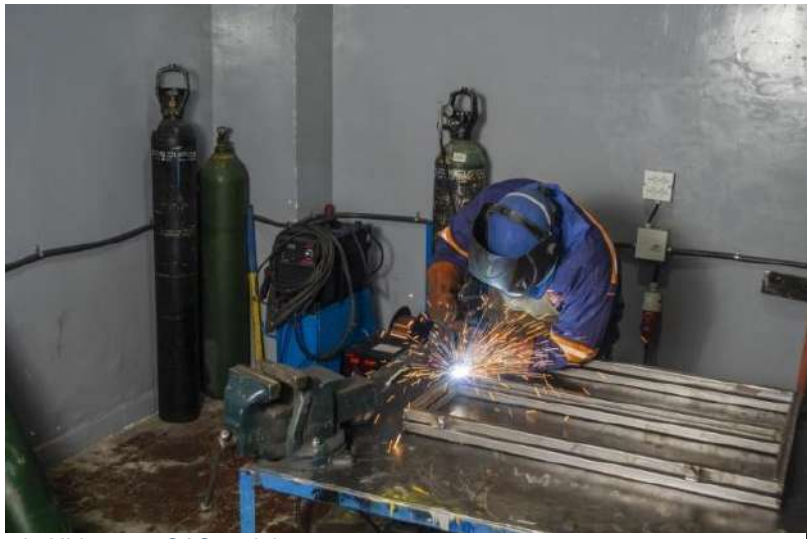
Soldador de Hidrateam SAS en labores
